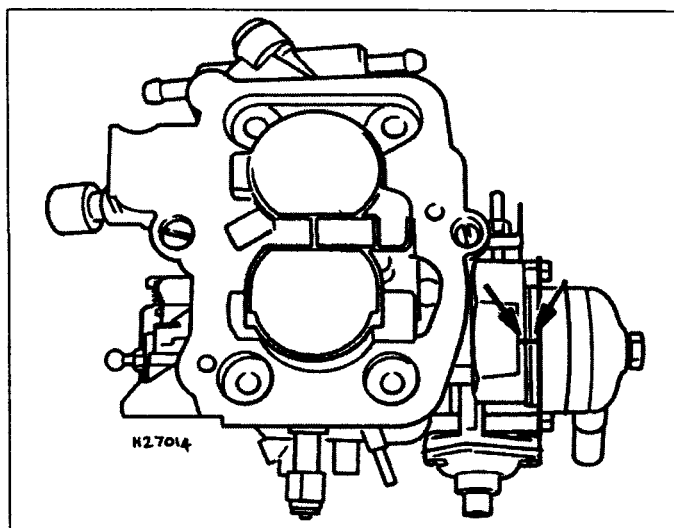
Метки совмещения корпуса и крышки пускового устройства
